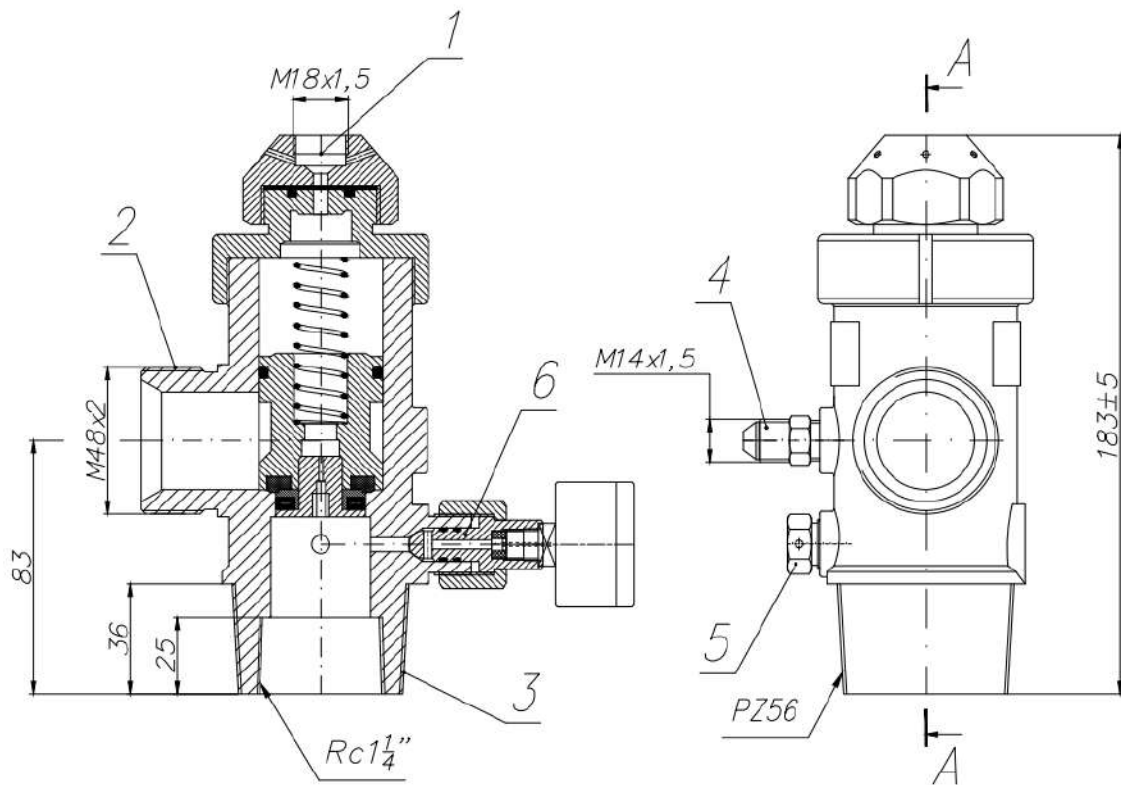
Общий вид запорно-пускового устройства QRF 32/6.7 с условным проходным диаметром DN32.
